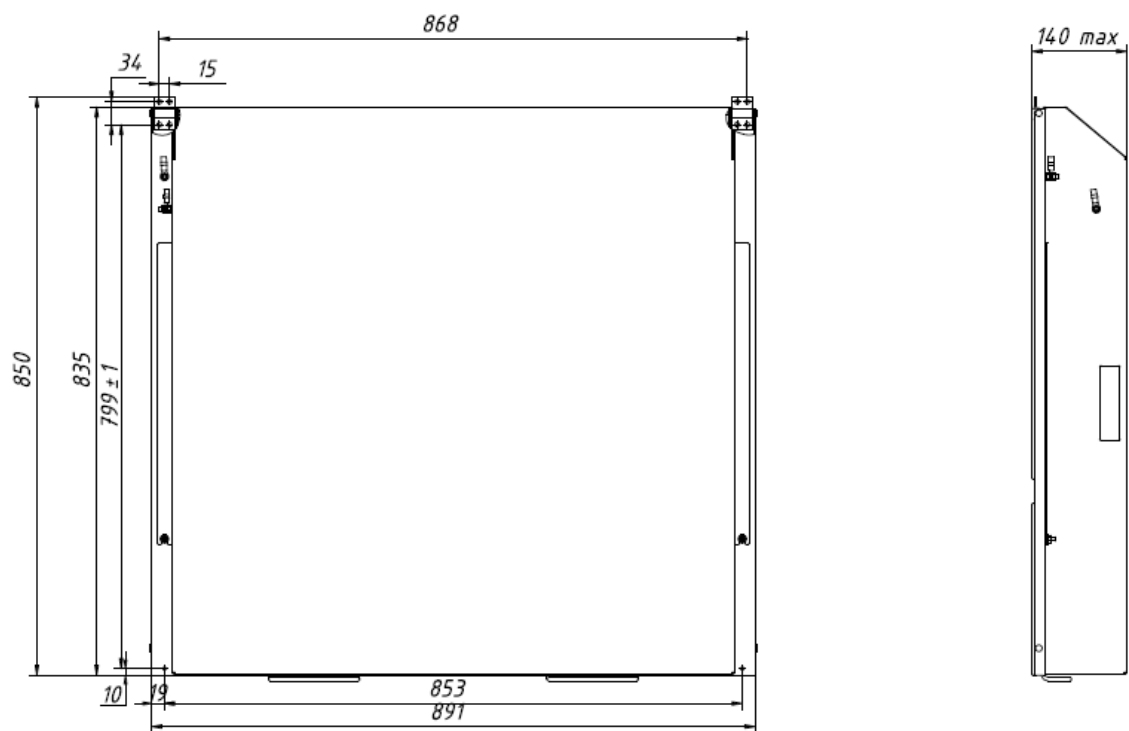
Габаритные чертежи ВЗУ-ЭЦС-М4
